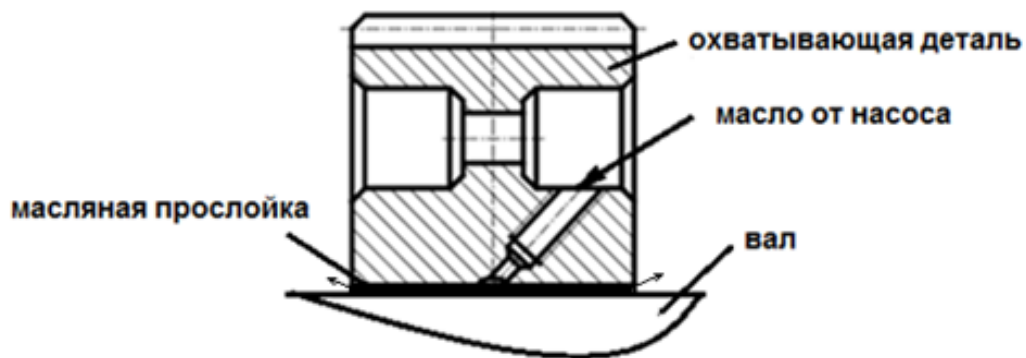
Гидропрессовый метод сборки соединений с натягом
